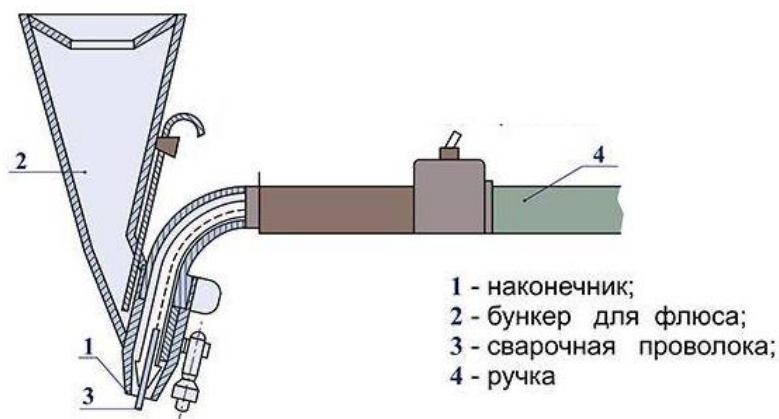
Держатель сварочного полуавтомата для сварки под флюсом
